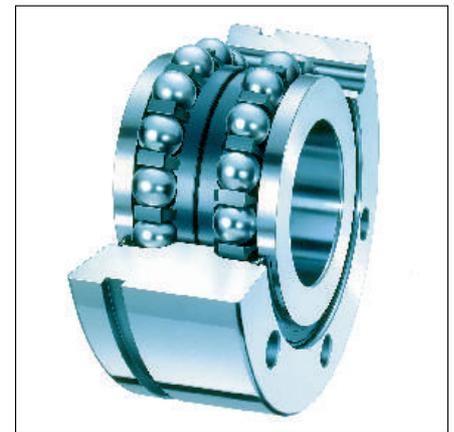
Un componente importante del soporte de ensayo es el rodamiento de dos hileras de bolas de contacto angular ZKLF de INA
